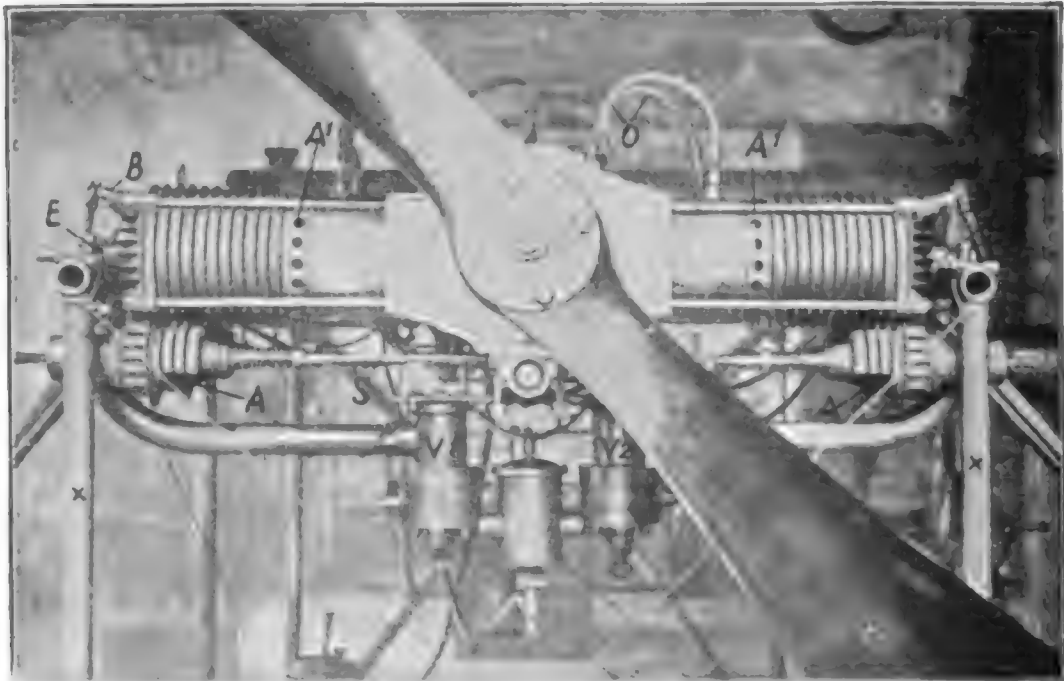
Flugmotor von Bertin. A Auspuffventil, A' freier Auspuff am Zylinder, E Einlaßventil, D Zündkerze, S Ventilstangen, V₁, V₂ Vergaser, C Ölrohre.
